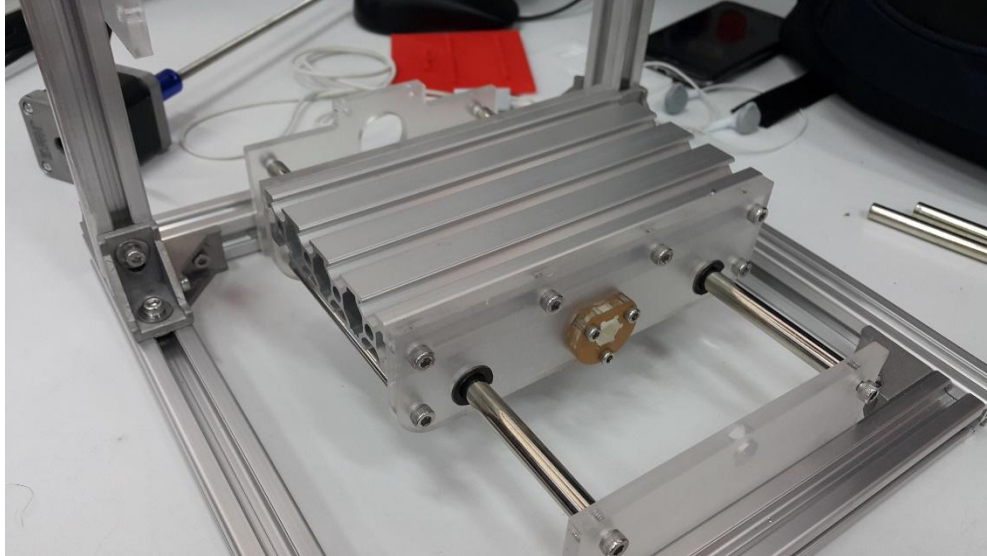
Ensamble del eje de rodamiento a la cama de fresado
